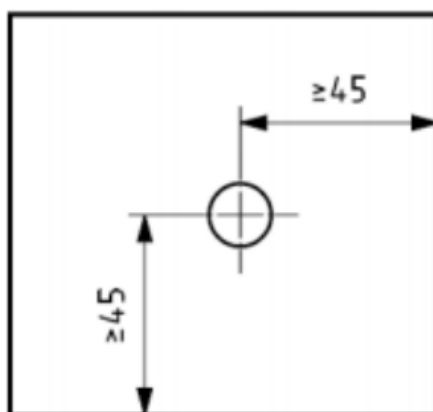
Plano de corte da amostra com 1 furo a 45 mm da borda
